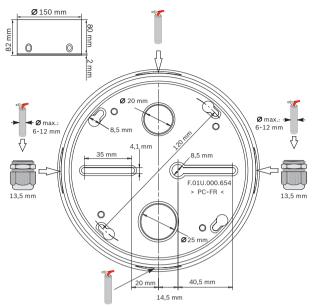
FAA-500-SB-H Boîtier arrière pour montage en surface
